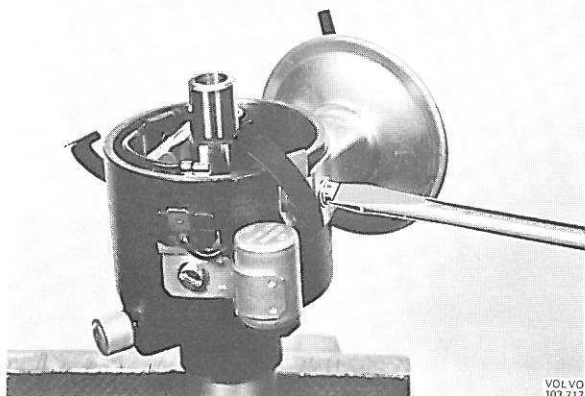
Démontage de régulateur à dépression, B 20 B
